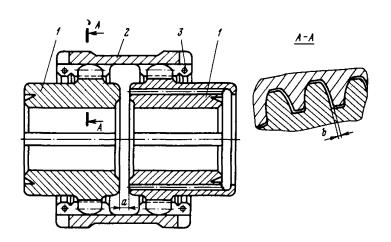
Зубчатая соединительная муфта: 1— зубчатая втулка; 2— зубчатая обойма; 3— пружинное кольцо
